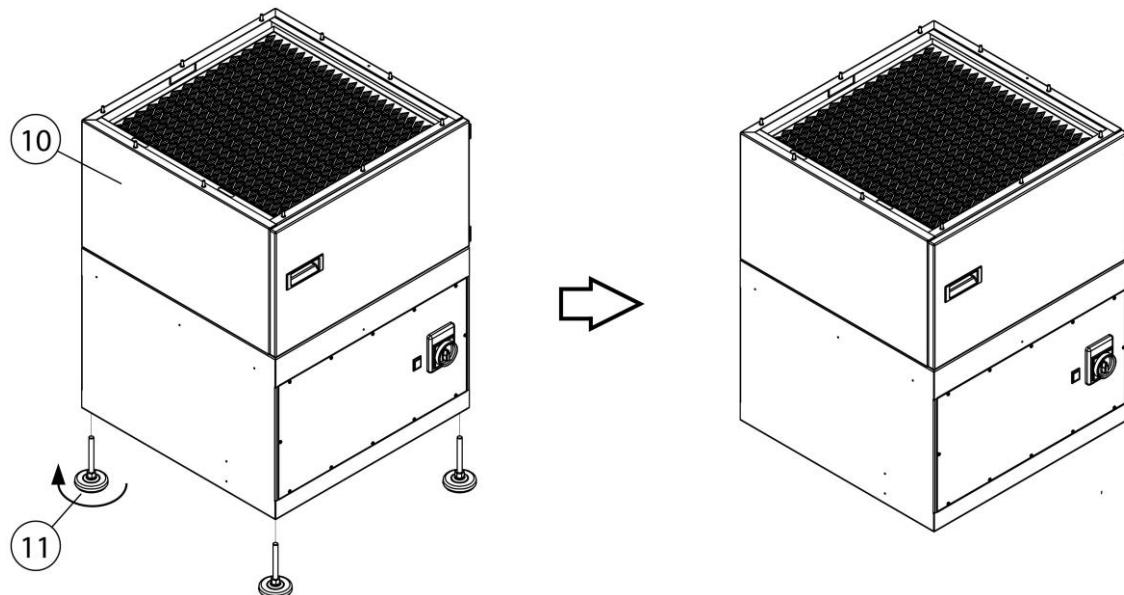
Montaggio - Smontaggio dei piedi di appoggio della macchina
